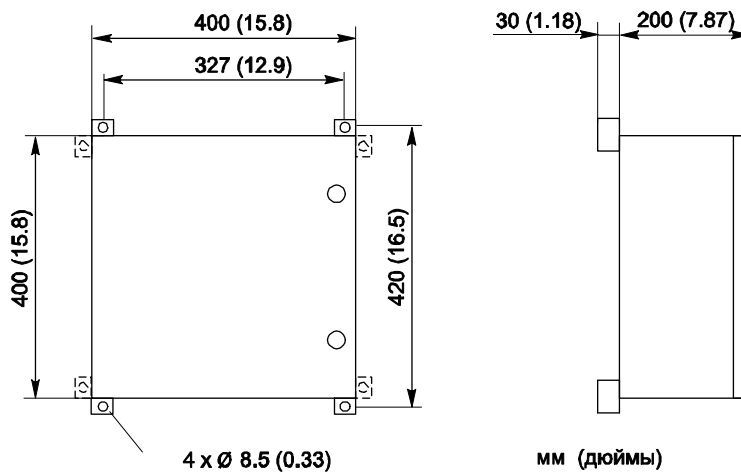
Размеры блока управления, левый главный вид, вид с правой стороны
